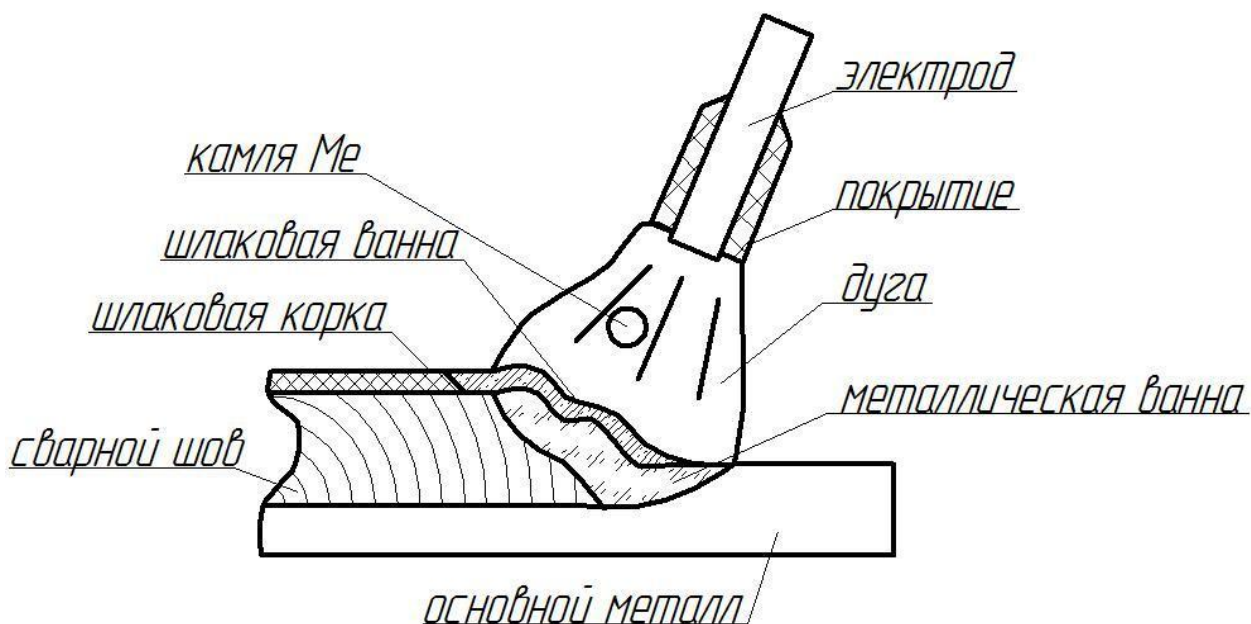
Дуговой сварки штучными электродами
